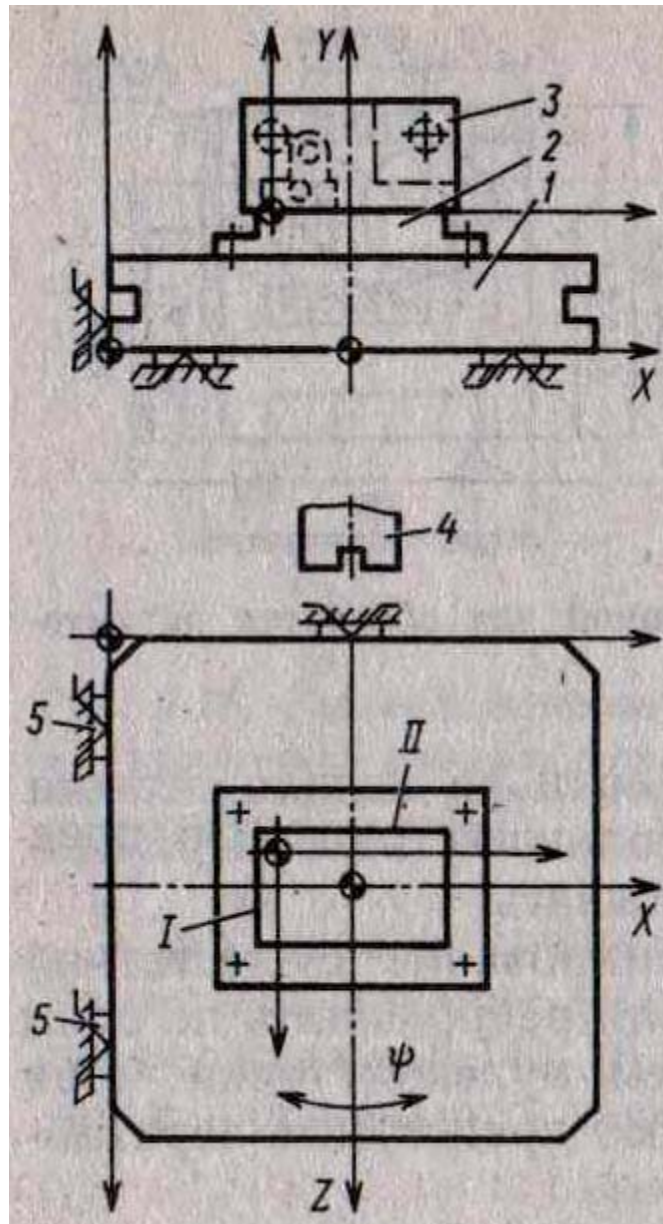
Установка заготовки на спутнике для выполнения второй операции
